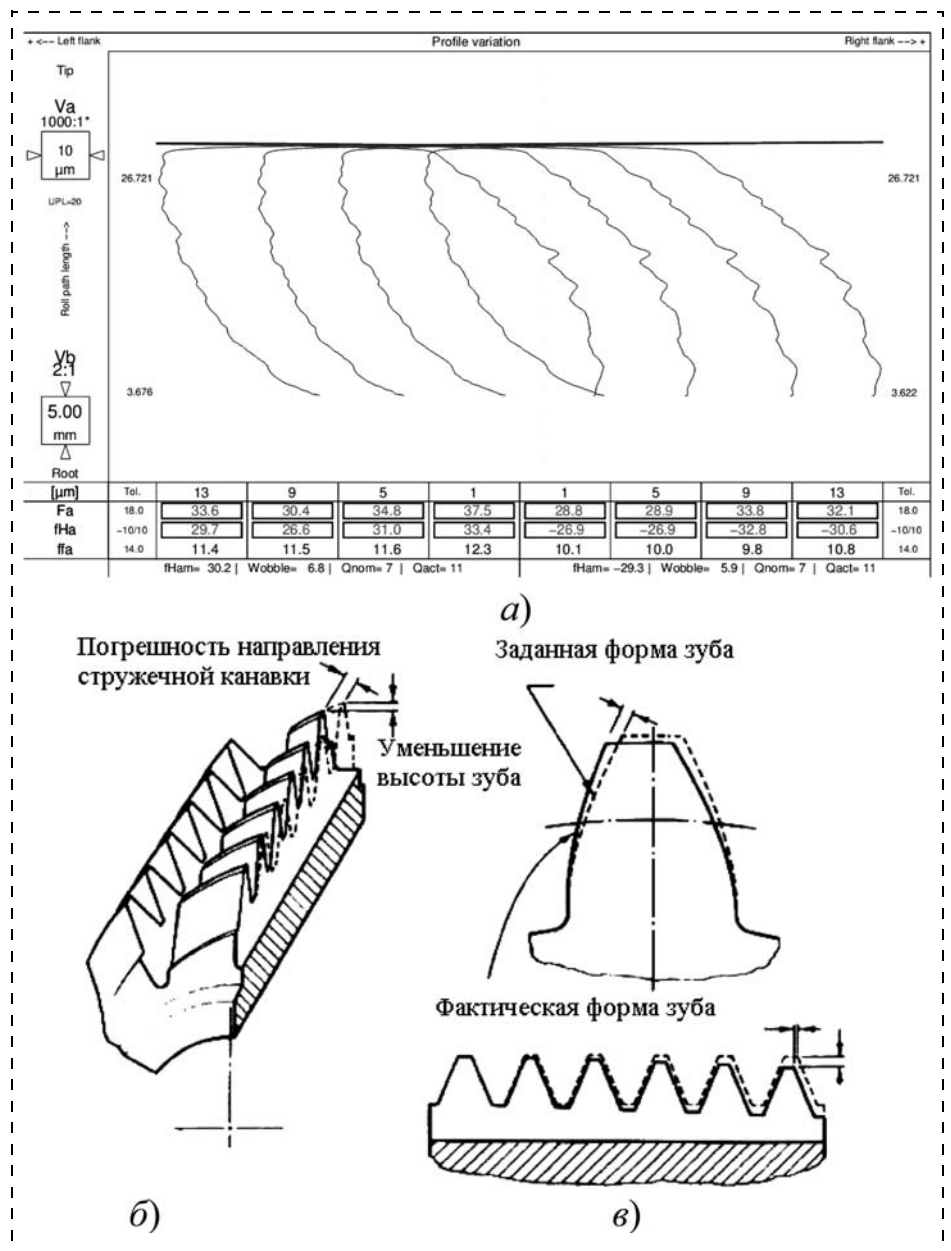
Влияние заточки фрезы на форму профиля зуба: а — фрагмент протокола измерения; б — профиль заточки фрезы; в — профиль зуба — наклонный зуб
